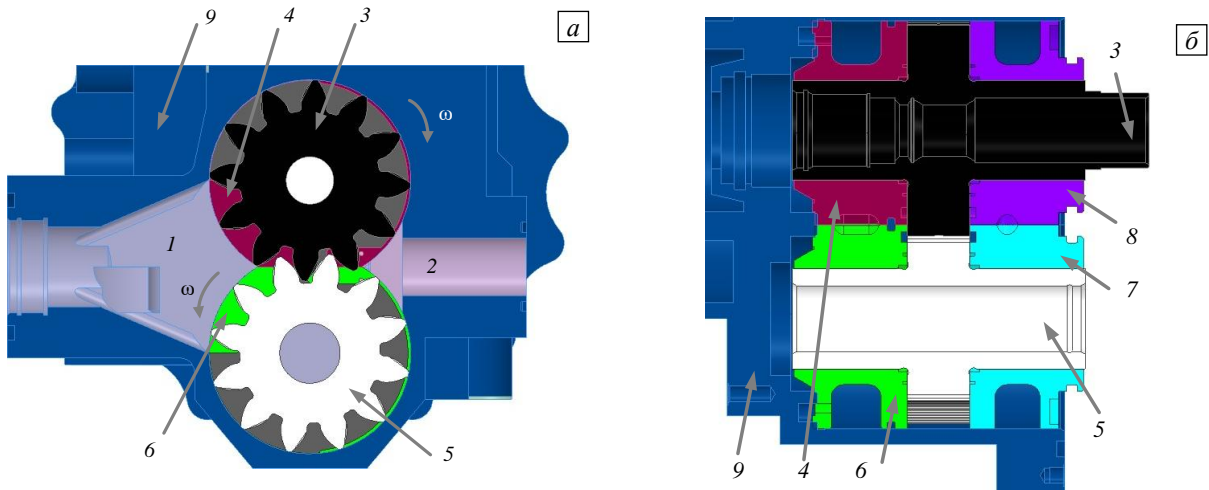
Схема шестеренного насоса – вид сверху (а) и вид сбоку (б): 1 – полость всасывания; 2 – полость нагнетания; 3 – ведущая шестерня; 5 – ведомая шестерня; 4, 6 – подшипники; 7, 8 – подпятники; 9 – корпус насоса
